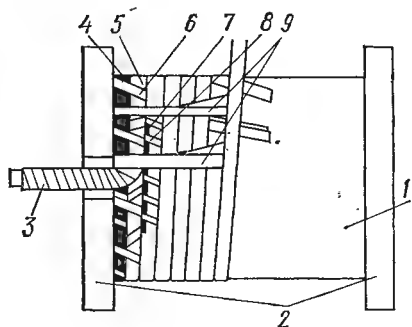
Крепление выводного конца и изоляции в обмотке:
